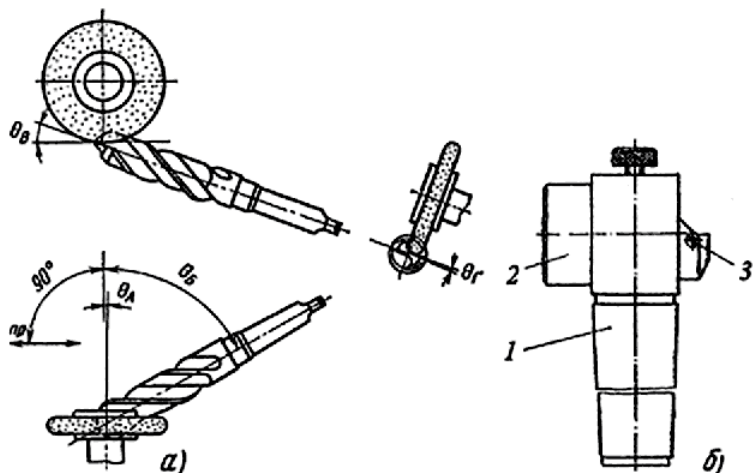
Схема установки шлифовального круга и сверла при подточке его поперечной кромки (а); оправка (б)
